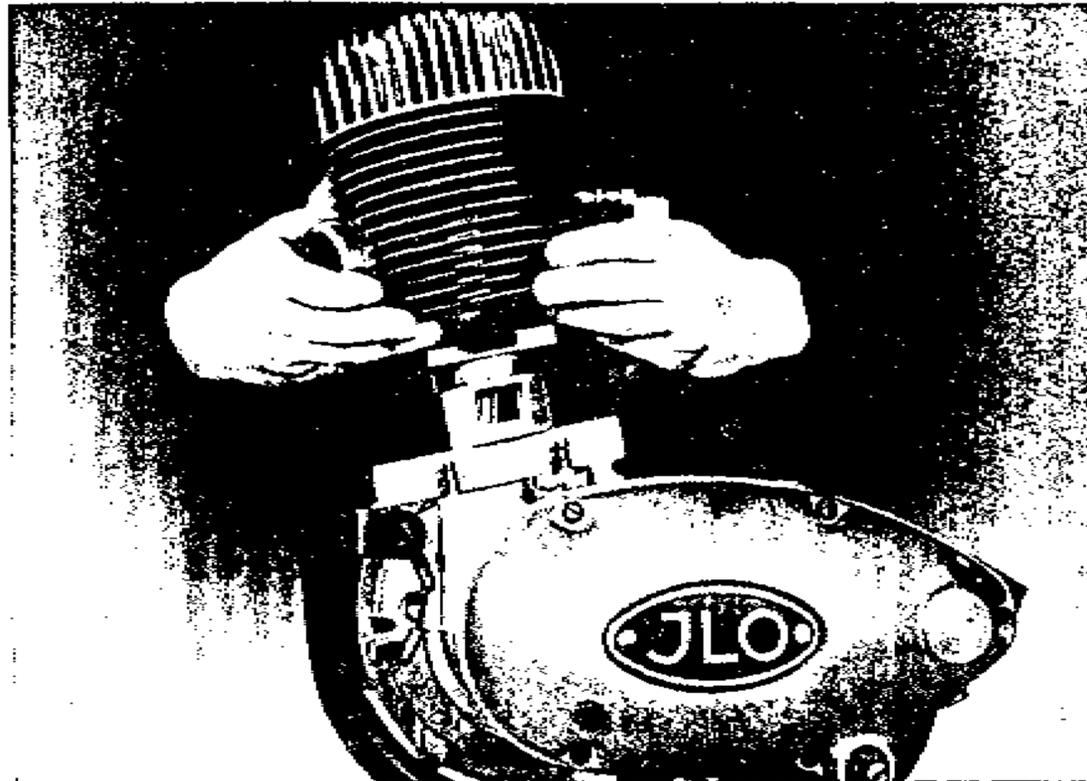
Demontage bzw. Montage des Zylinders. Unterlegen des U-förmigen Montageholzes.
